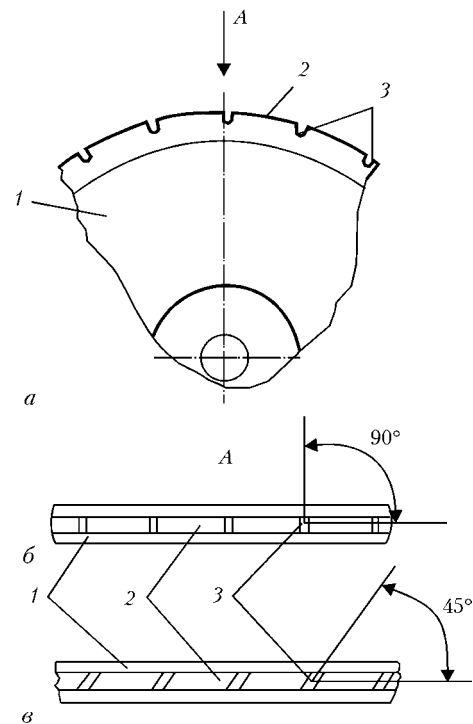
Схема выполнения прорезей на рабочей дорожке диска-холодильника: *а* — вид сбоку; *б* — прорези, параллельные оси вращения диска; *в* — прорези под углом 45°; 1 — боковая поверхность; 2 — рабочая дорожка; 3 — прорези
